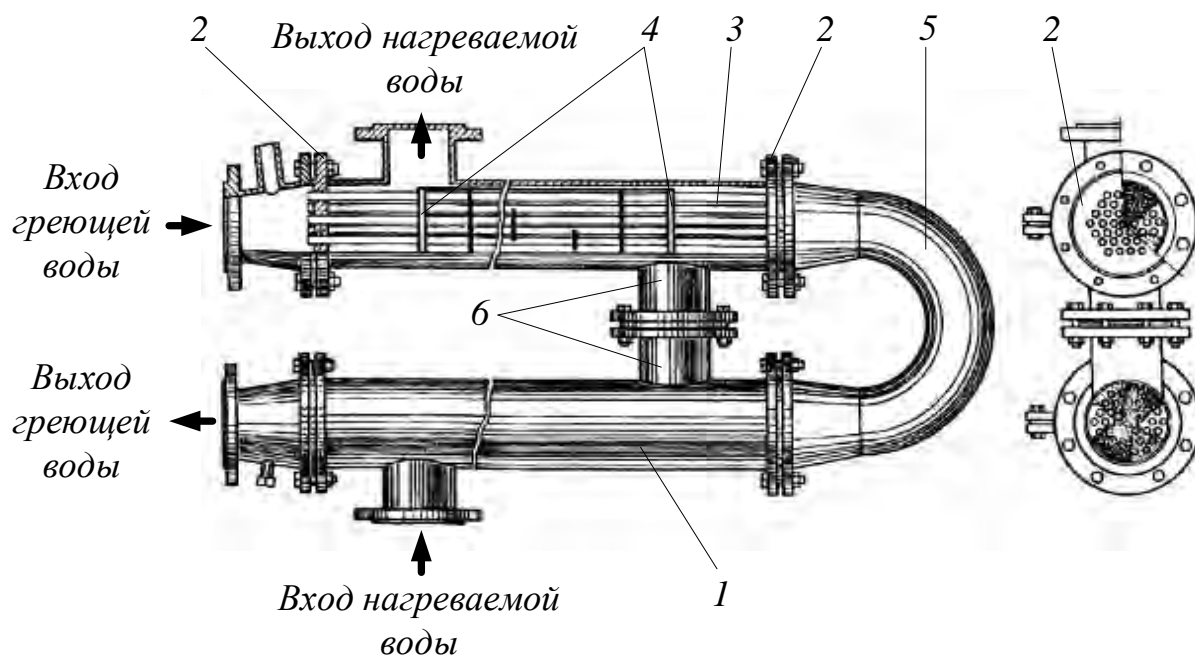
Скоростной водяной подогреватель: 1 – корпус; 2 – трубные доски; 3 – трубный пучок; 4 – опорные кольца; 5 – соединительный калач; 6 – переходной патрубок
